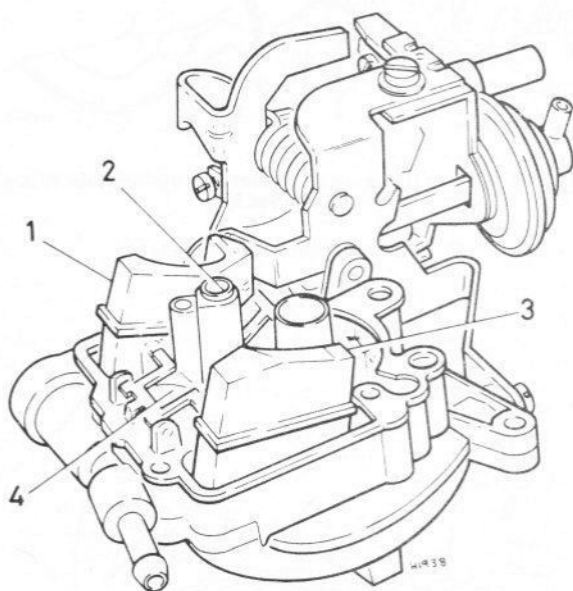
Couvercle supérieur retourné - carburateur Weber 36 TLC (Sec 8)
